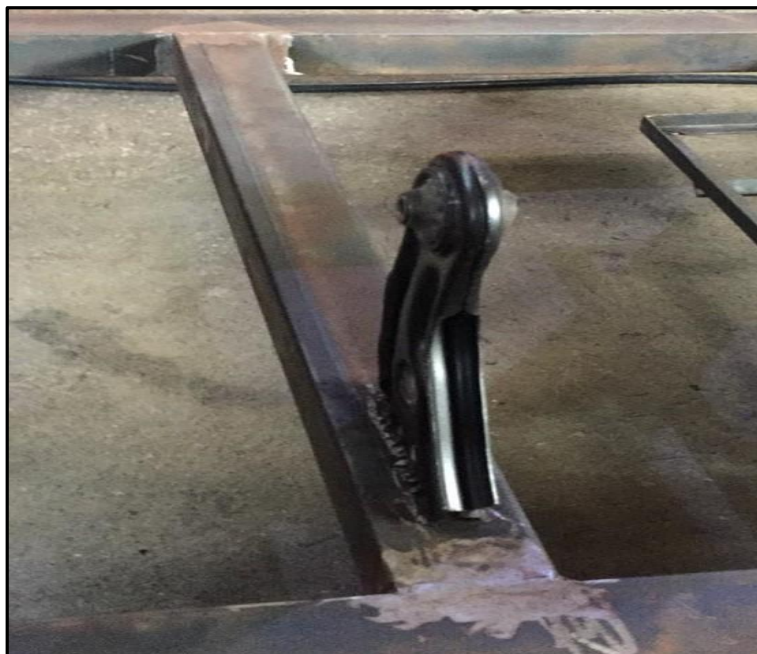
Soldadura de la base inferior para la caja de cambios
